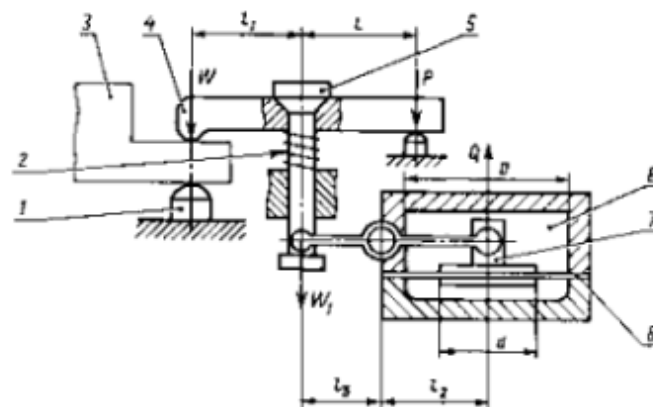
Комбинированное зажимное устройство с пневмоприводом. W - сила, зажима; Q - сила на штоке пневмокамеры; P - реакция опоры.
